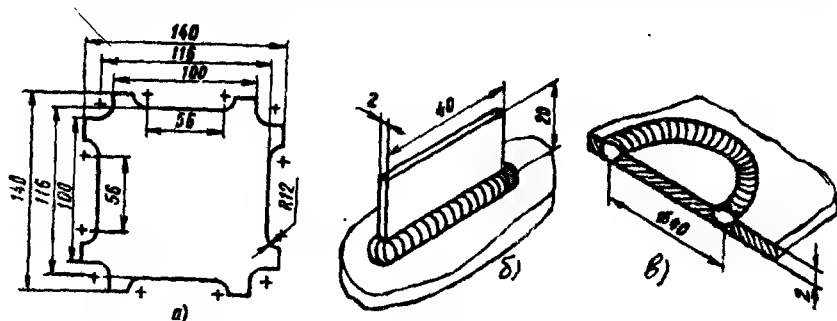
Плоские образцы для испытаний на двухосное растяжение: а — из основного металла; б — с приваренным ребром; в — с круговым швом
